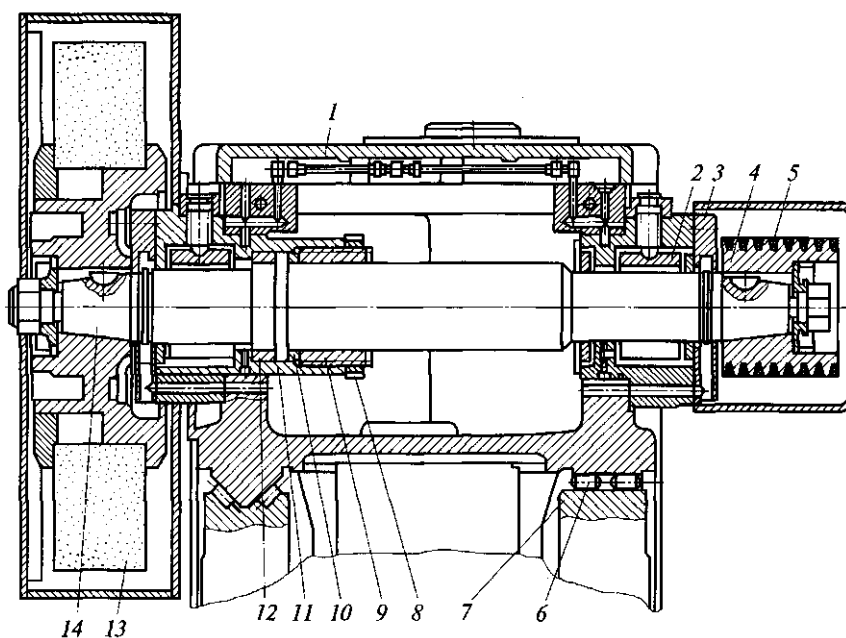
Шлифовальная бабка круглошлифовального полуавтомата: 1 — корпус; 2 — подшипник скольжения; 3 — крышка; 4 — шкив; 5 — клиноременная передача; 6 — направляющие качения; 7 — станина; 8 — контргайка; 9 — гайка; 10, 12 — кольца; 11 — обойма; 13 — шлифовальный круг; 14 — шпиндель
